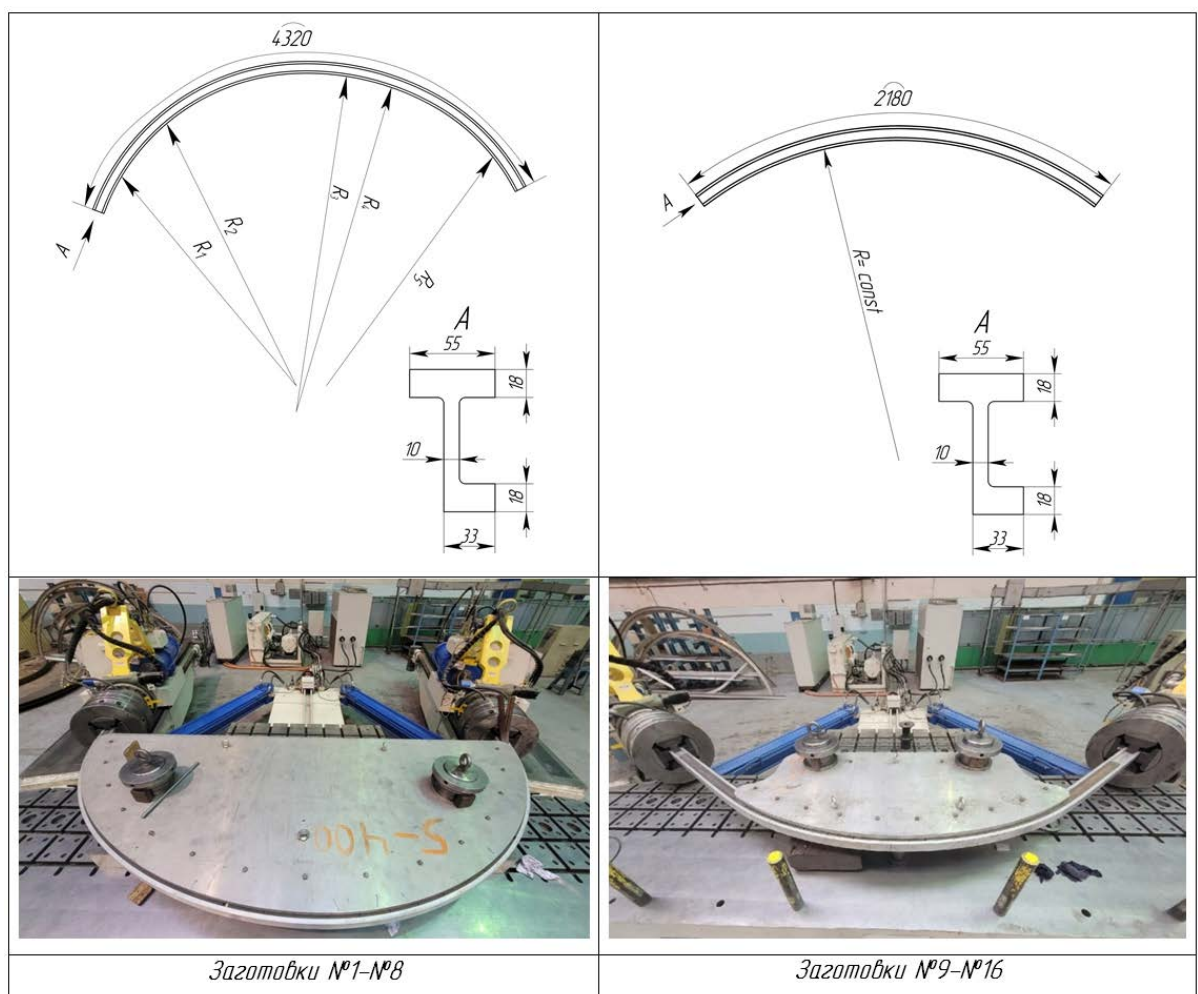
Эскизы заготовок сегментов шпангоута и внешний вид деформированных заготовок на прессе V-80
